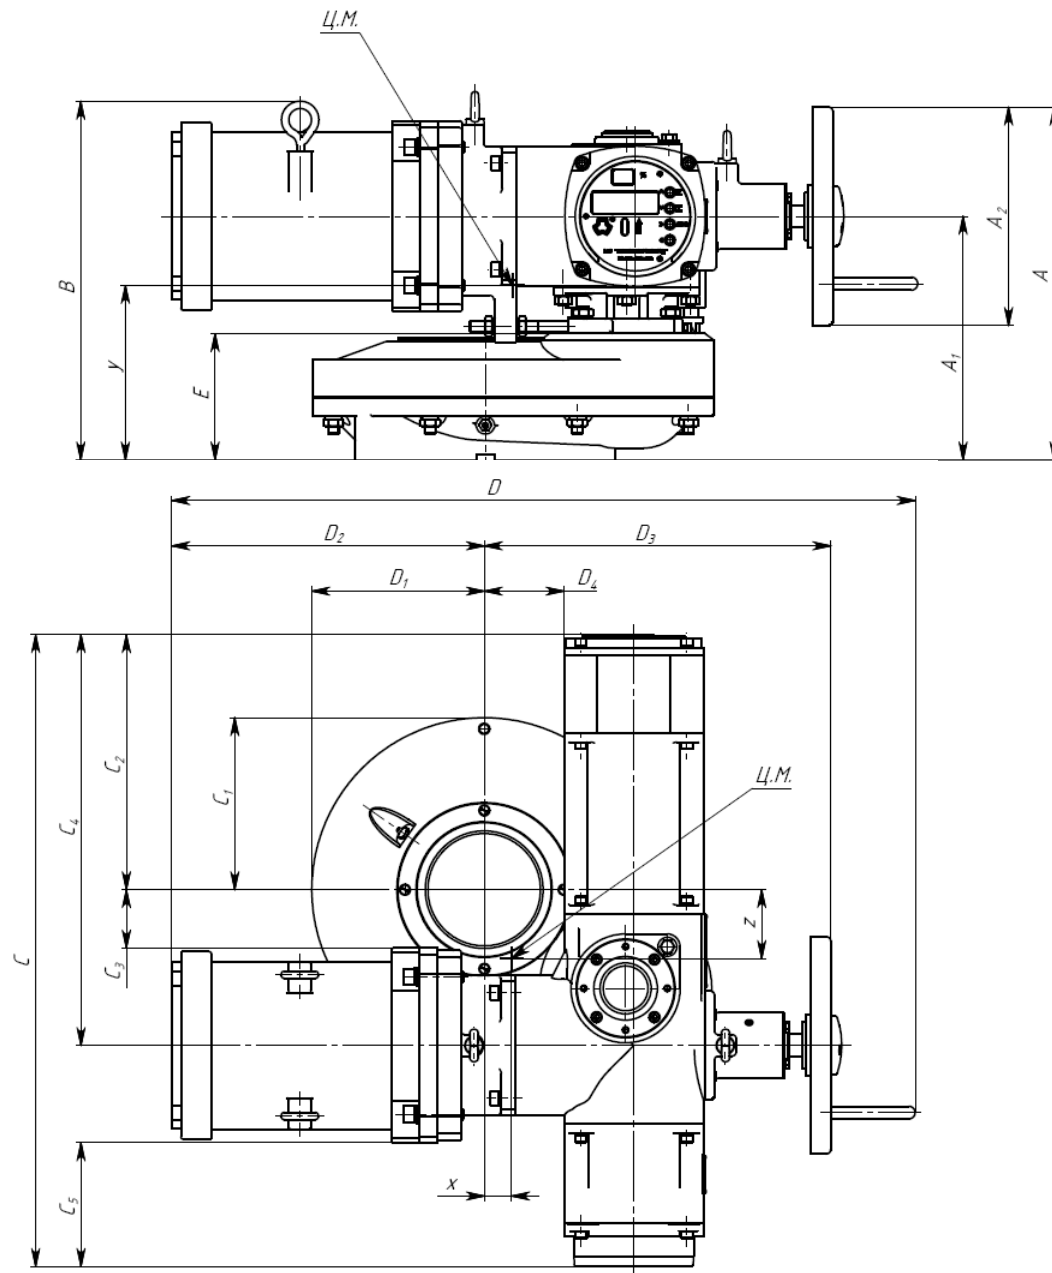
б – Габаритные размеры привода конструктивной схемы 410
